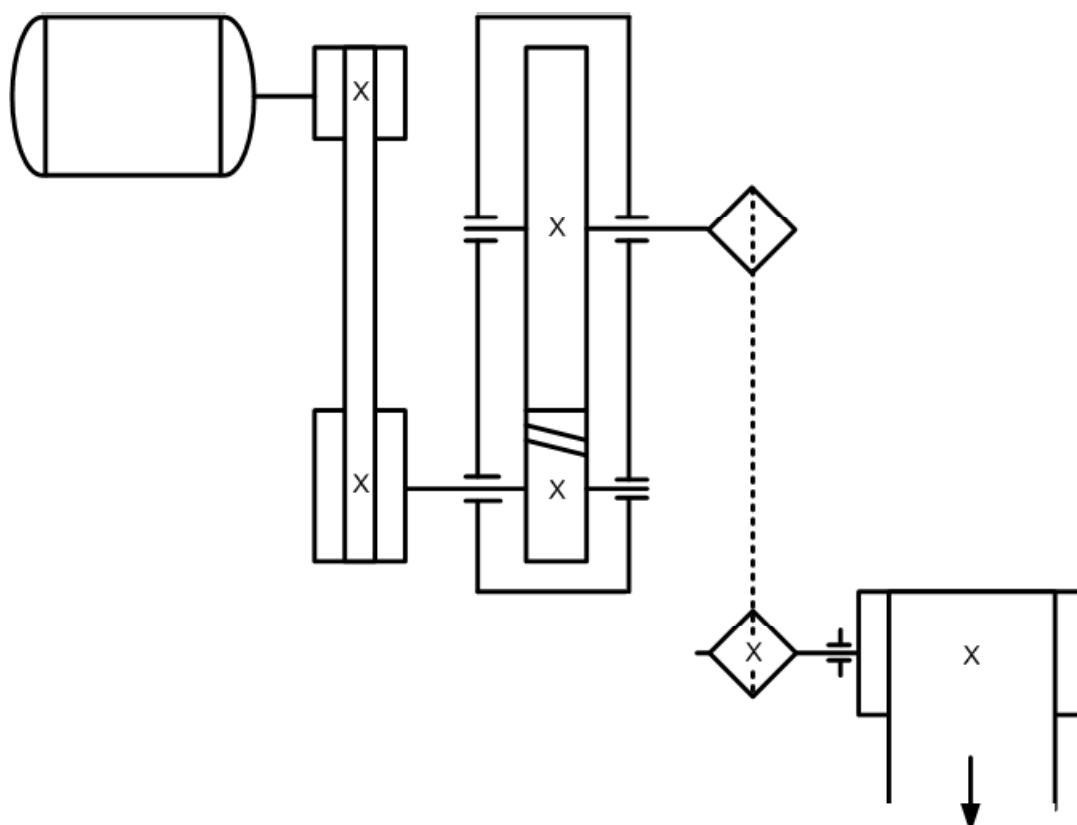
Кинематическая схема трехступенчатого привода ленточного конвейера
